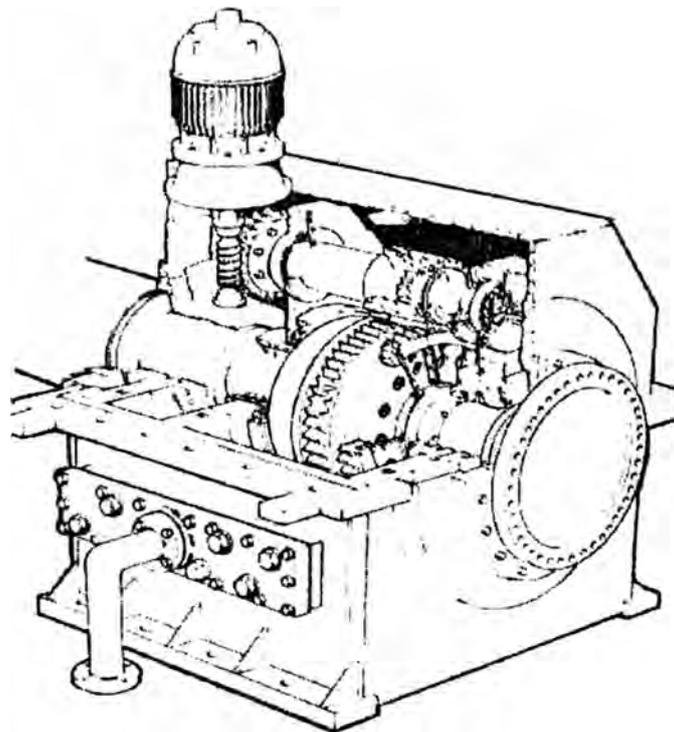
Esquema de disposición del embrague para incorporación del motor de arranque.
